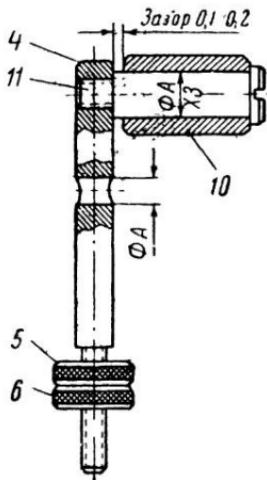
Модель плоскоременной передачи с натяжным роликом (схема соединения деталей натяжного устройства): 4 — рычаг натяжного устройства; 5 — гайка (груз); 6 — контргайка (груз); 10 — натяжной ролик; 11 — ось натяжного ролика.
